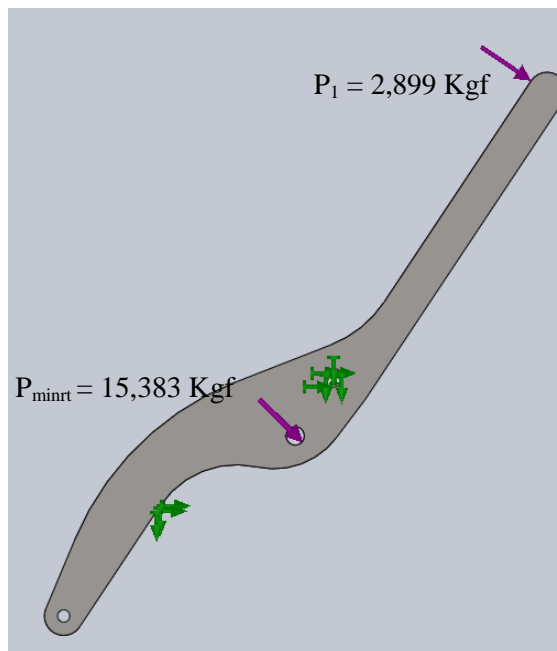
Cargas aplicadas en el eslabón al final del centrado.
